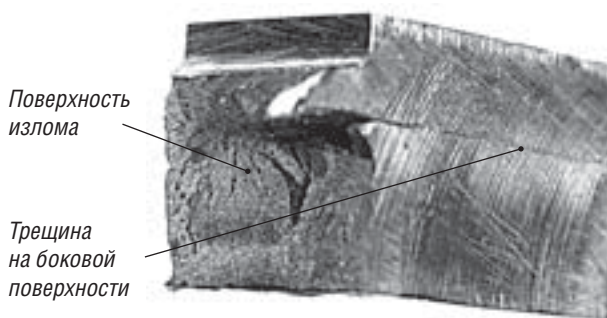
Внешний вид половины ударного образца, изготовленного из болта М30х220 после испытаний
